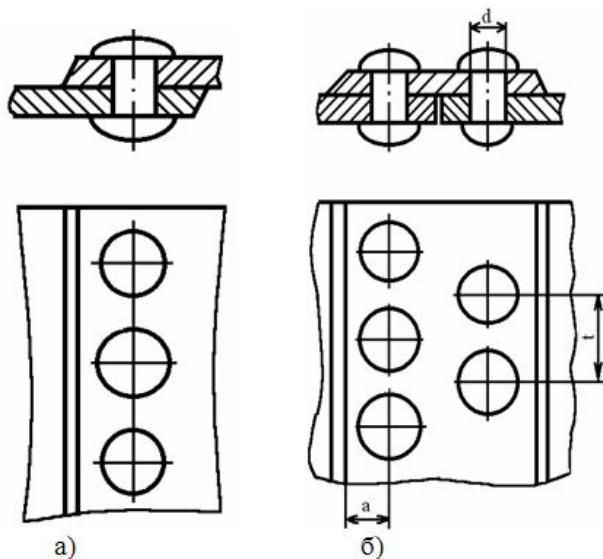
Розташування заклепок у з'єднаннях
